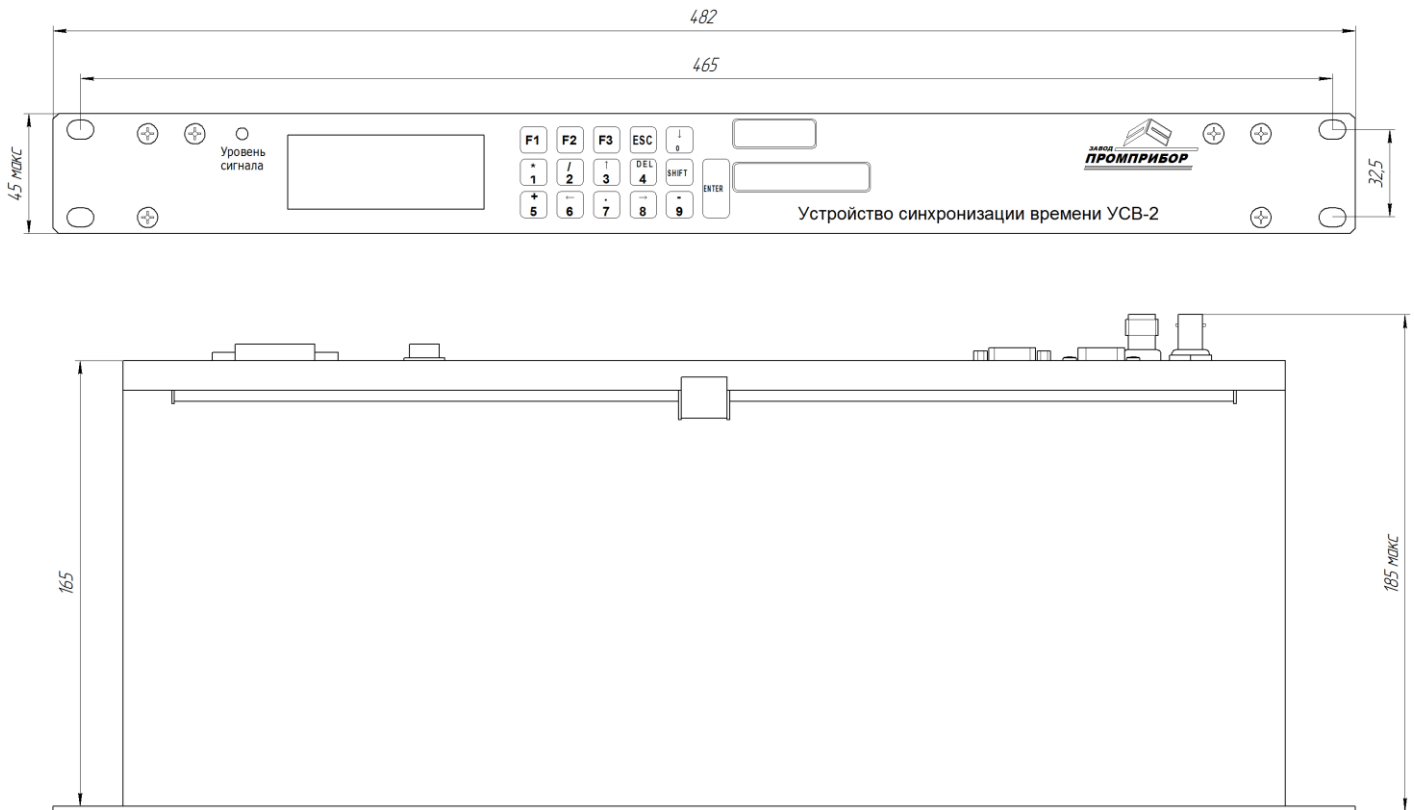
Габаритные и установочные размеры УСВ-2 в Корпусе 19"
